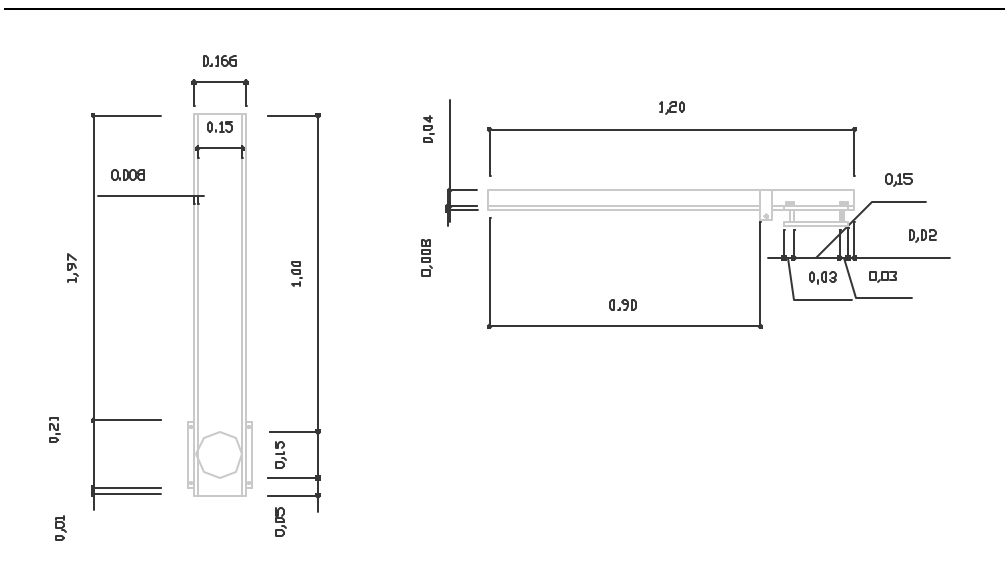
Detalhes da rampa: Planta baixa e corte lateral.(medidas em metros).
